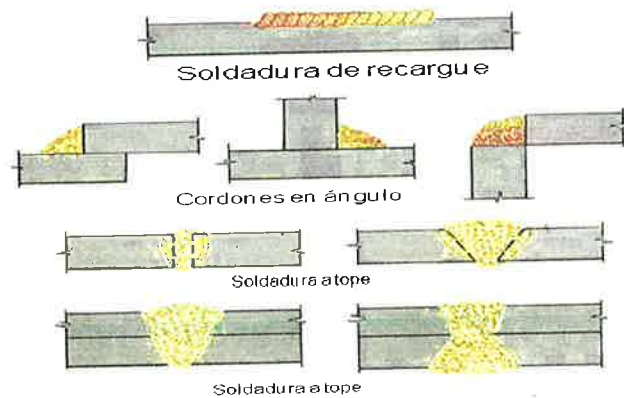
Representación esquemática de los tipos de soldaduras.
